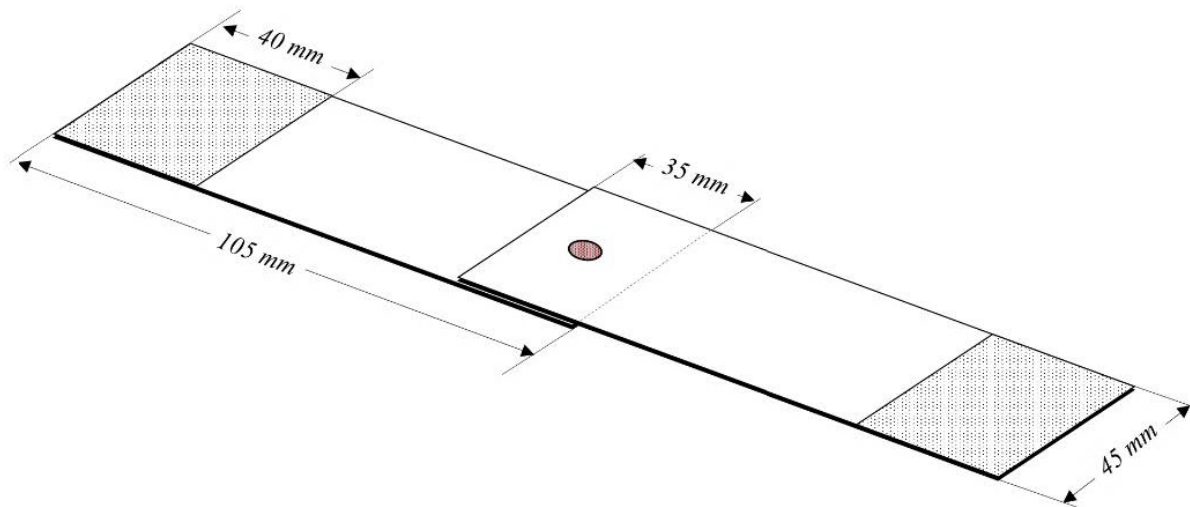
Dimensões dos corpos de prova utilizados. Adaptado de [42].
